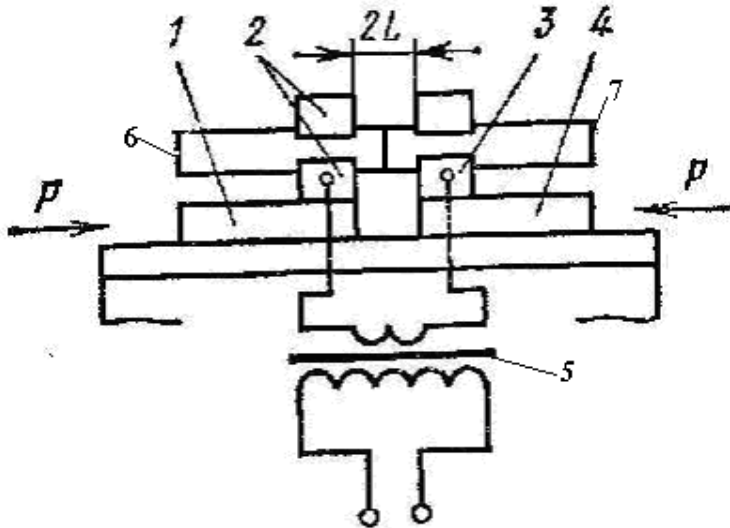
Схема контактной стыковой сварки: 1 – неподвижная плита, 2, 3 – зажимы, 4 – подвижная плита, 5 – сварочный трансформатор, 6, 7 – свариваемые заготовки
